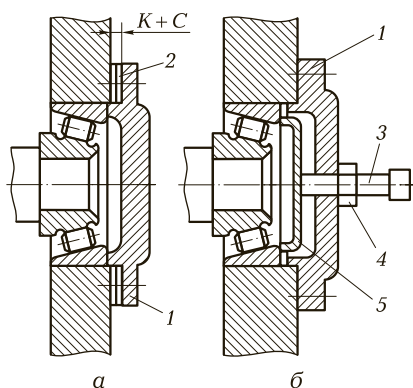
Схема регулирования радиально-упорного роликового подшипника:
